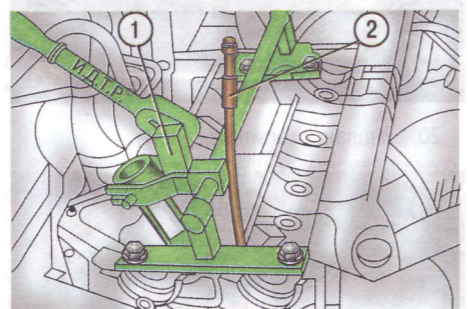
Приспособления для снятия пружин клапанов: 1 - приспособление для сжатия пружин; 2 - приспособление для подачи воздуха в свечное отверстие
